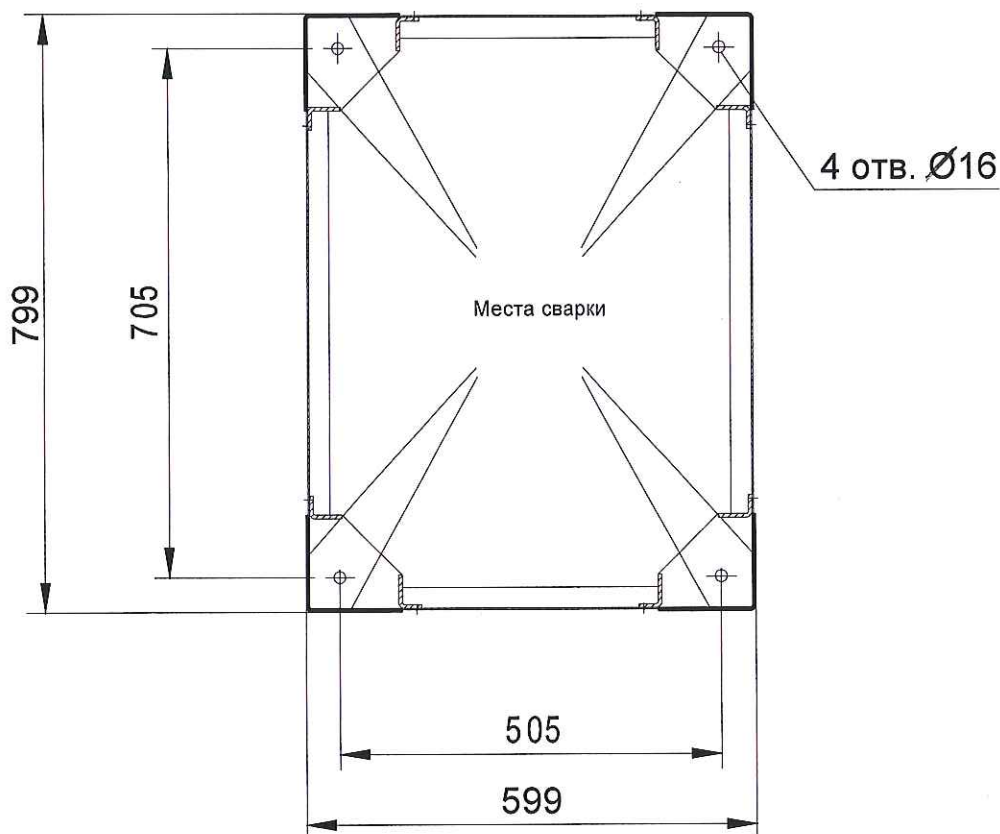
Габаритные и установочные размеры цоколя приборного шкафа
